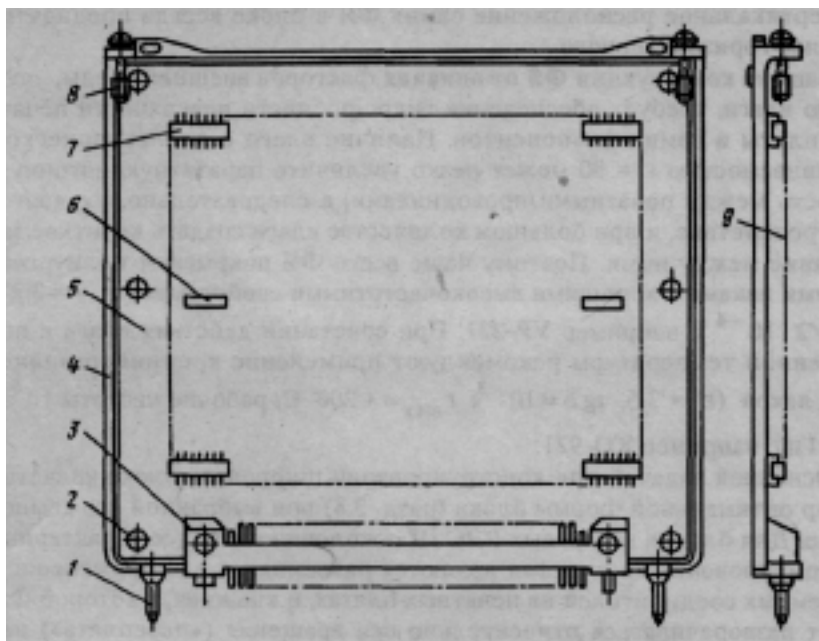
Конструкция ФЯ блока разъемного типа:
